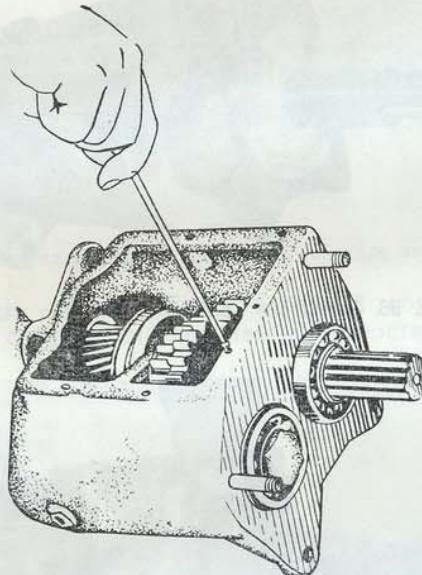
Установка стопорного винта оси блока шестерен заднего хода
